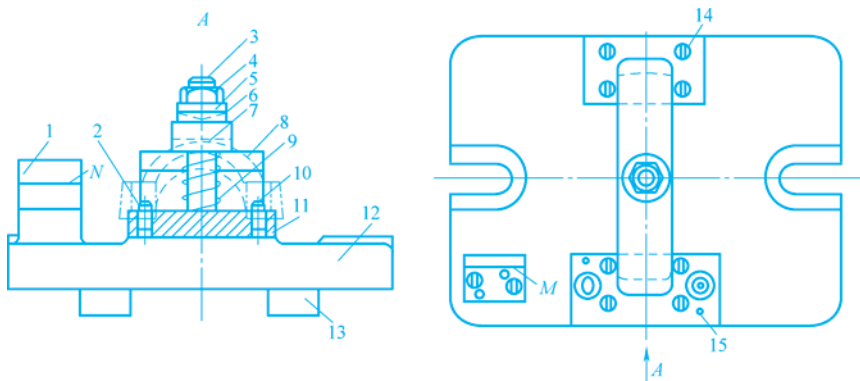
铣削连杆盖凹台面的专用铣床夹具
